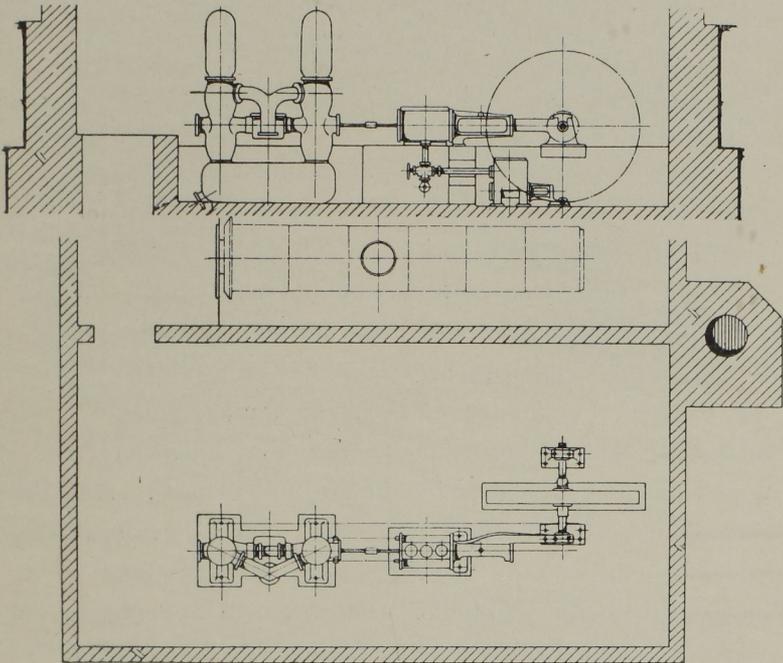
Seitenansicht und Grundriss der Maschine in Florenz.
